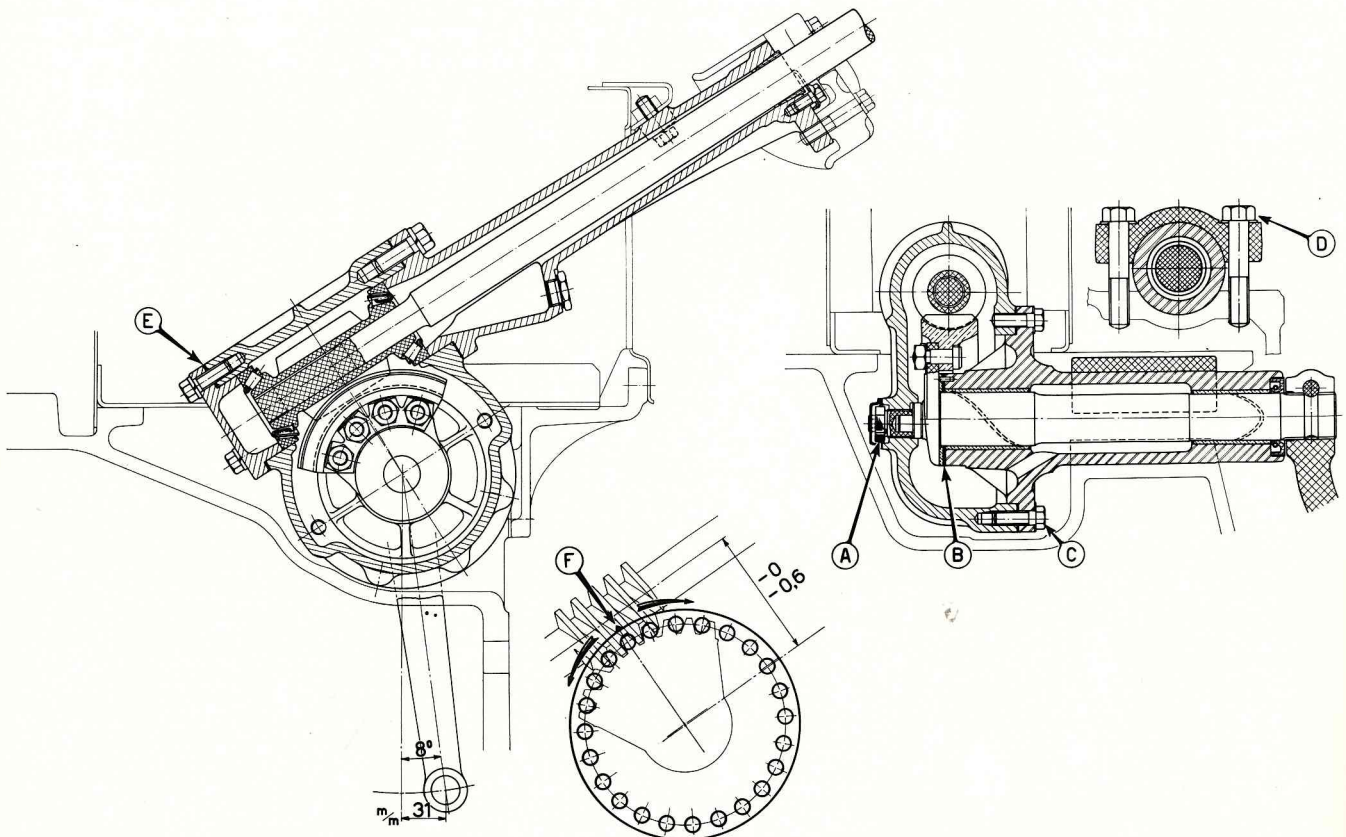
Sezione longitudinale e trasversale sulla scatola sterzo.
